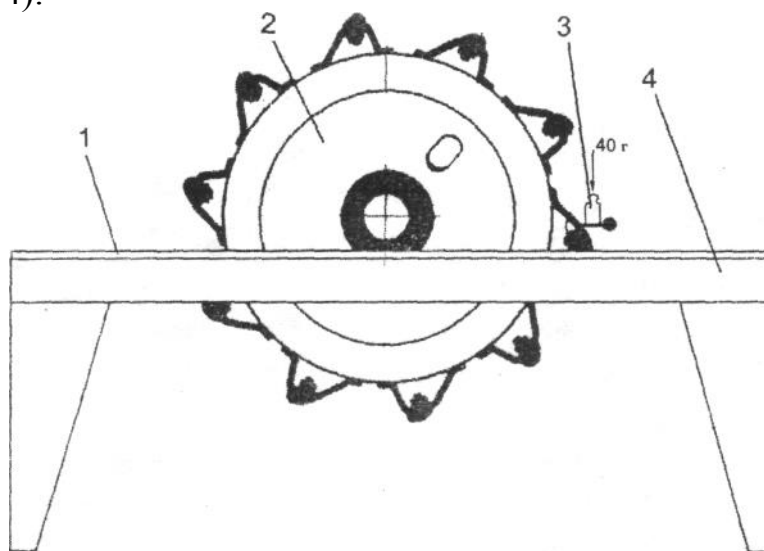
Схема приспособления для статической балансировки молотильного барабана:
